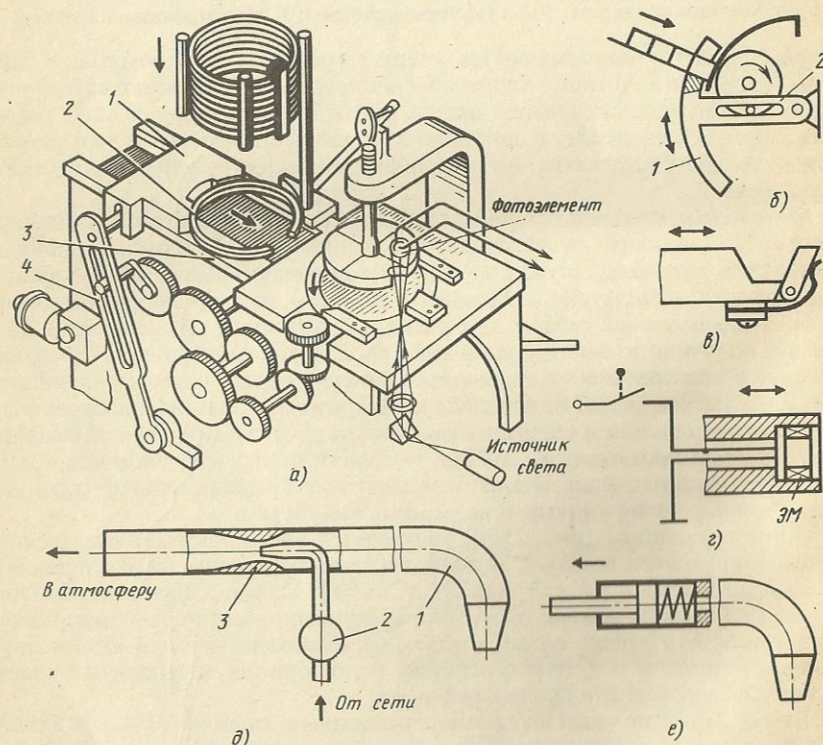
Схема автооператора для сортировки поршневых колец и конструктивные варианты толкателей
